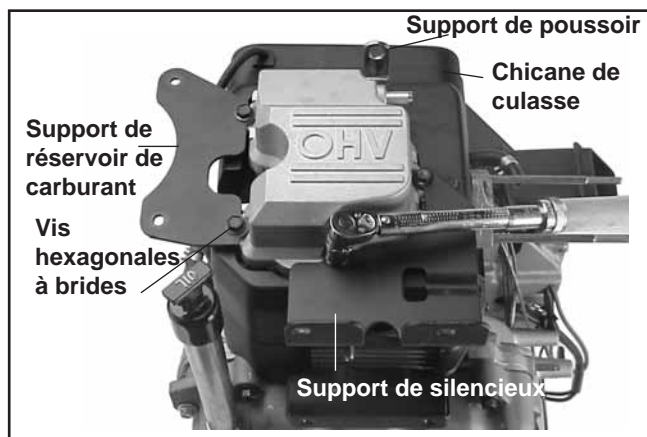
Installation du couvercle de soupape. (Couvercle en aluminium moulé sous pression montré).
